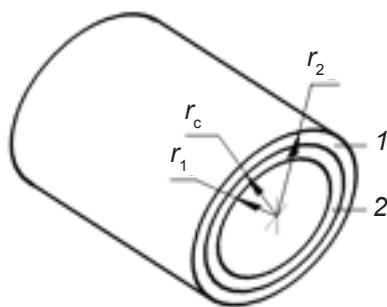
Схема цилиндрической комбинированной отливки: 1 – отливка; 2 – керамическая вставка
